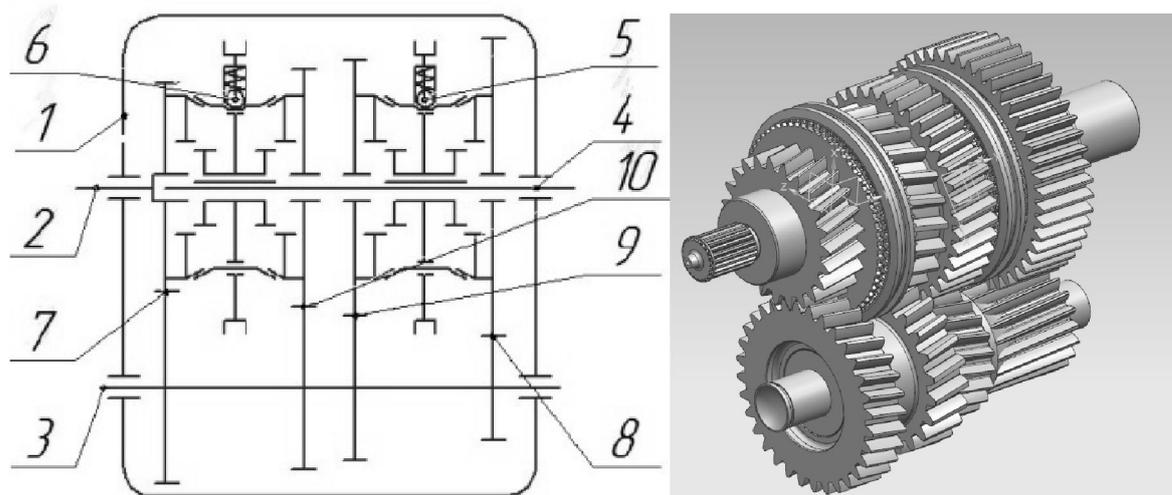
Кинематическая схема и конструкция основного редуктора:
